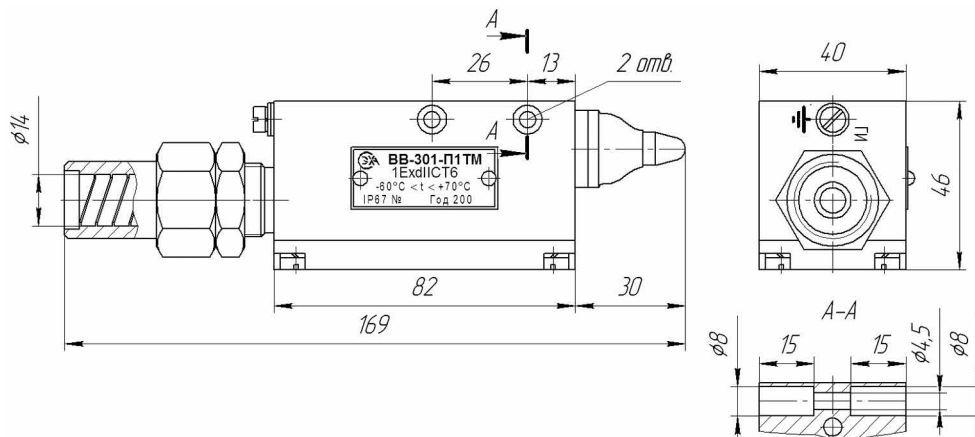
Габаритные и установочные размеры ВВ-301-П1ТМ
